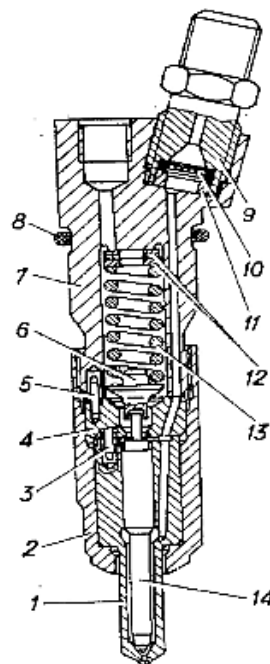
Будова форсунки: 1 – корпус розпилювача; 2 – гайка розпилювача; 3,5 – встановлювальні штифти; 4 – прокладка; 6 – штанга; 7 – корпус; 8 – ущільнювальне кільце; 9 –штуцер; 10 – фільтр; 11 – ущільнювальна втулка; 12 – регулювальні шайби; 13 – пружина; 14 – голка розпилювача.
